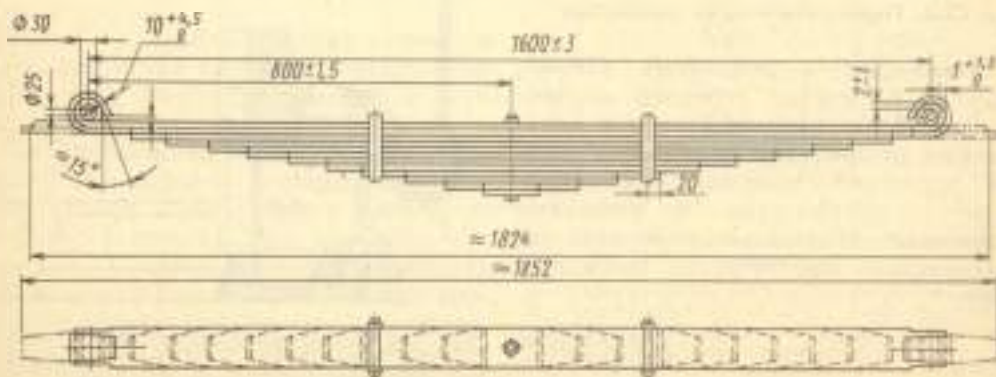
Передняя листовая рессора в сборе и ее размеры
